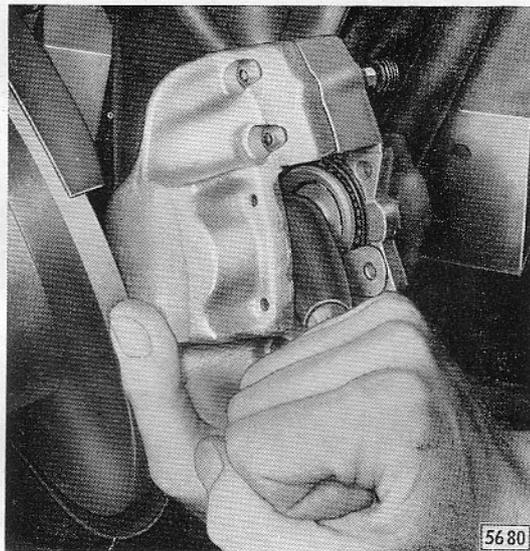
Verdrehsicherungsblech in Kolben eindrücken
